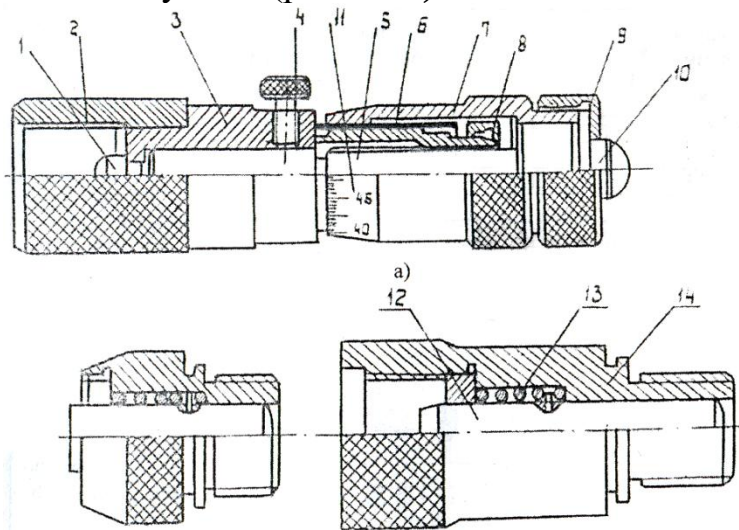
Мікрометричний нутромір: 1. П'ята (вимірювальний наконечник); 2. Внутрішня різьба; 3. Стебло; 4. Стопор; 5. Хвостовик мікрометричного гвинта; 6. гільза; 7. Барабан; 8. Регулююча гайка; 9. Затяжна гайка; 10. Мікрометричний гвинт; 11. Шкала; 12. Стержень; 13. Пружина; 14. Трубка
